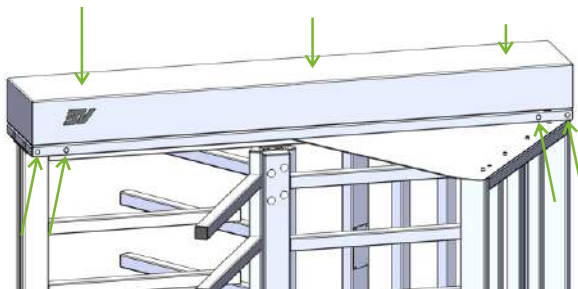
Турникет с надетой крышкой корпуса механизма
